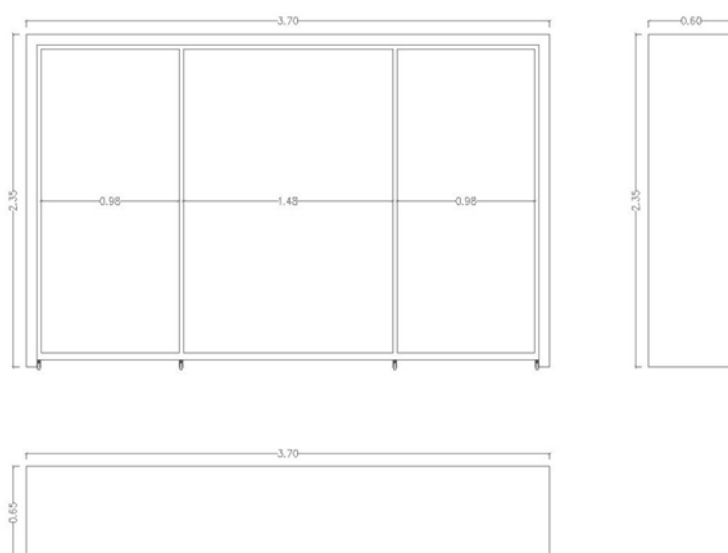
Estrutura base do móvel. Planta e alçados.
